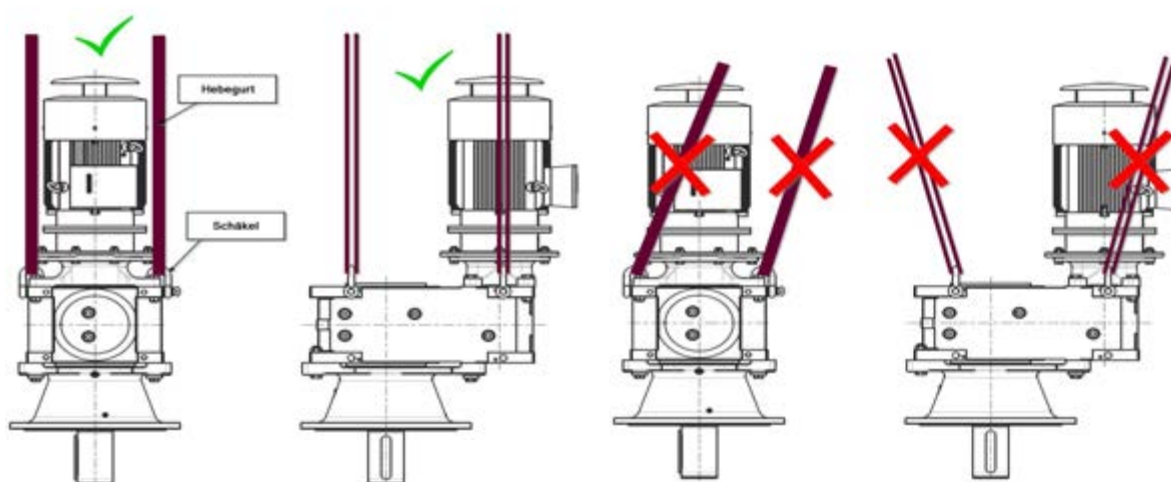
Транспортировка редуктора с механизмом для перемешивающих устройств
